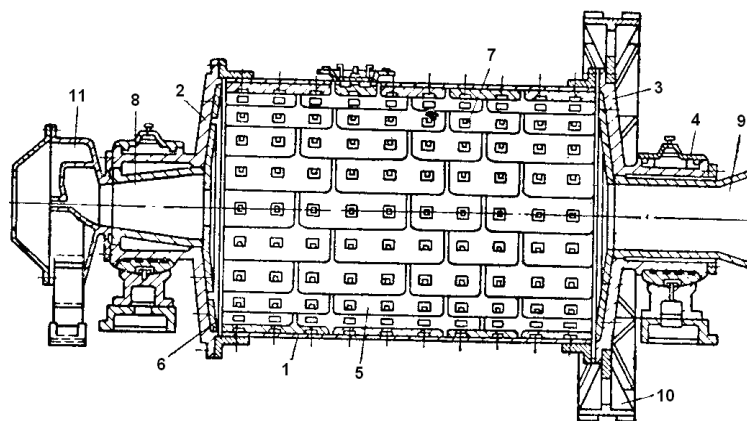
Шаровая мельница с центральной разгрузкой
